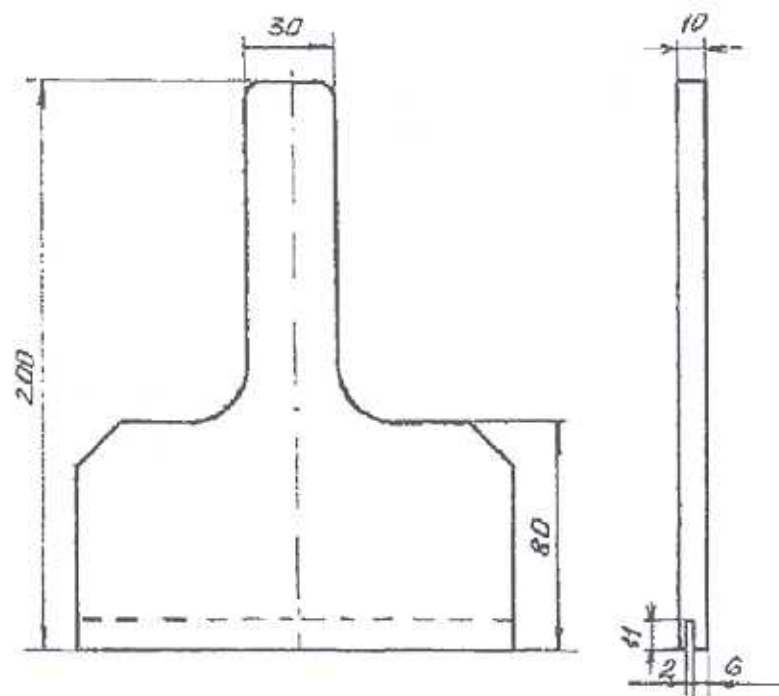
Оправка для установки уплотняющих прокладок в пазы статора
